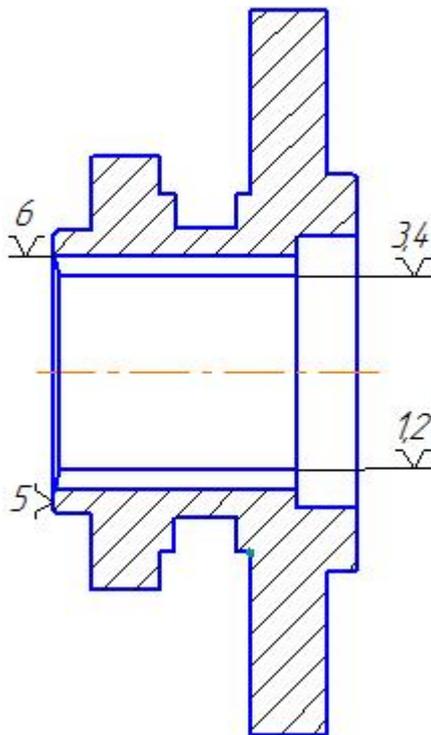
Схема базирования детали при установке на шлицевую оправку
